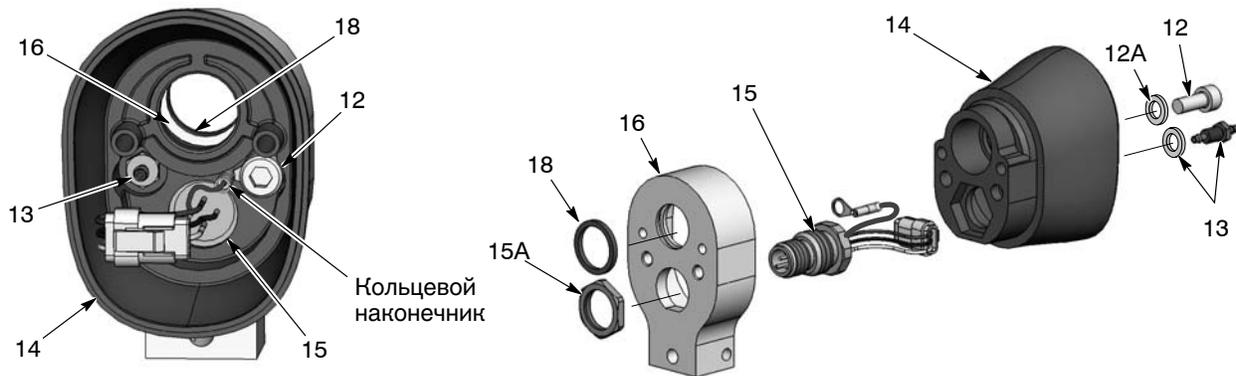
Распылитель для монтажа на штанге, разборка, 3 из 3
